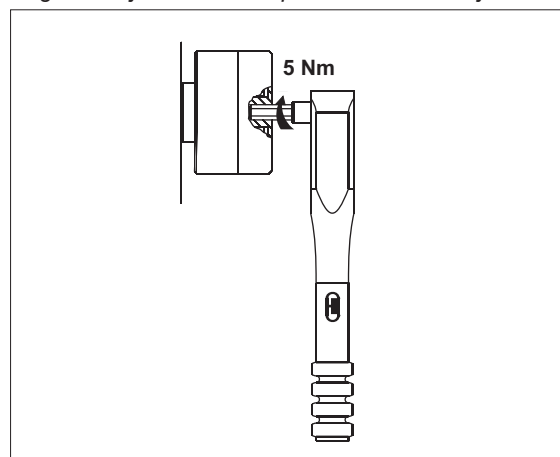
Apretar la tapa de la carcasa con una llave dinamométrica
